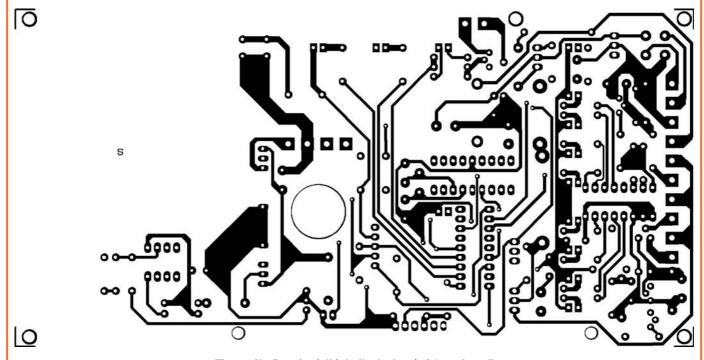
Dessin, à l'échelle 1, du côté "soudures" du circuit imprimé double face de la platine principale de l'antivol domestique à deux zones.
